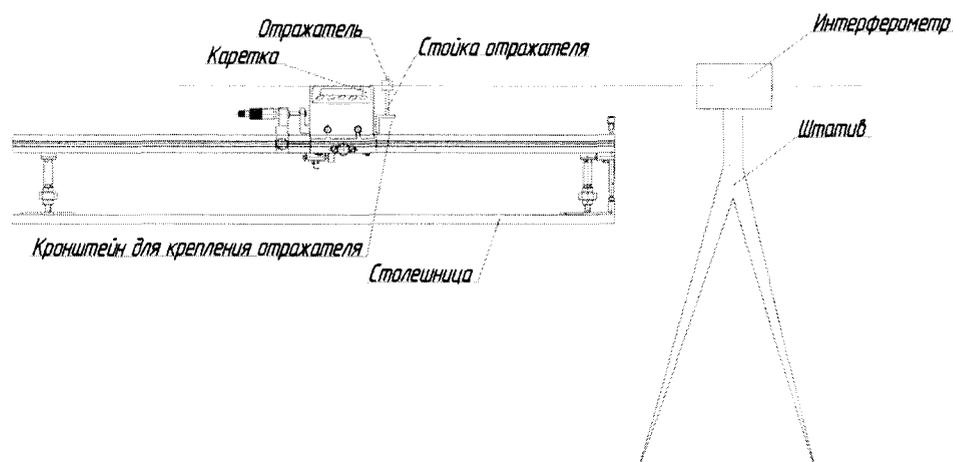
Схема установки интерферометра и отражателя при поверке установки
